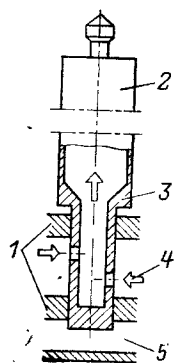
Способ крепления ТВС — гидравлический затвор:
